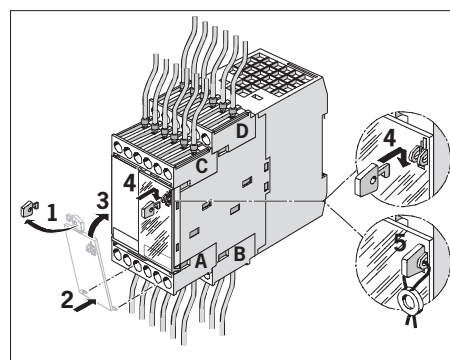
Installazione ed apposizione dei sigilli della lastra di protezione
